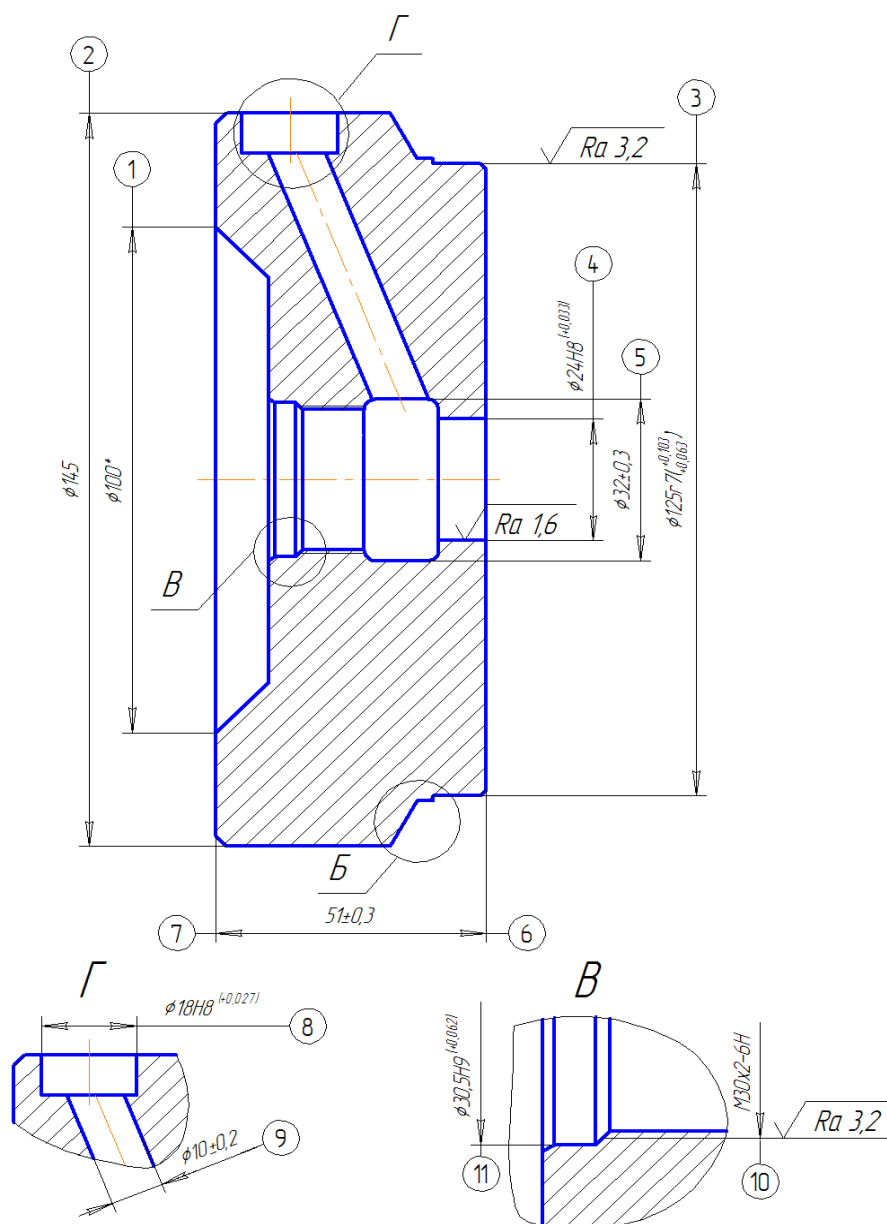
Эскиз детали «Крышка цилиндра»
